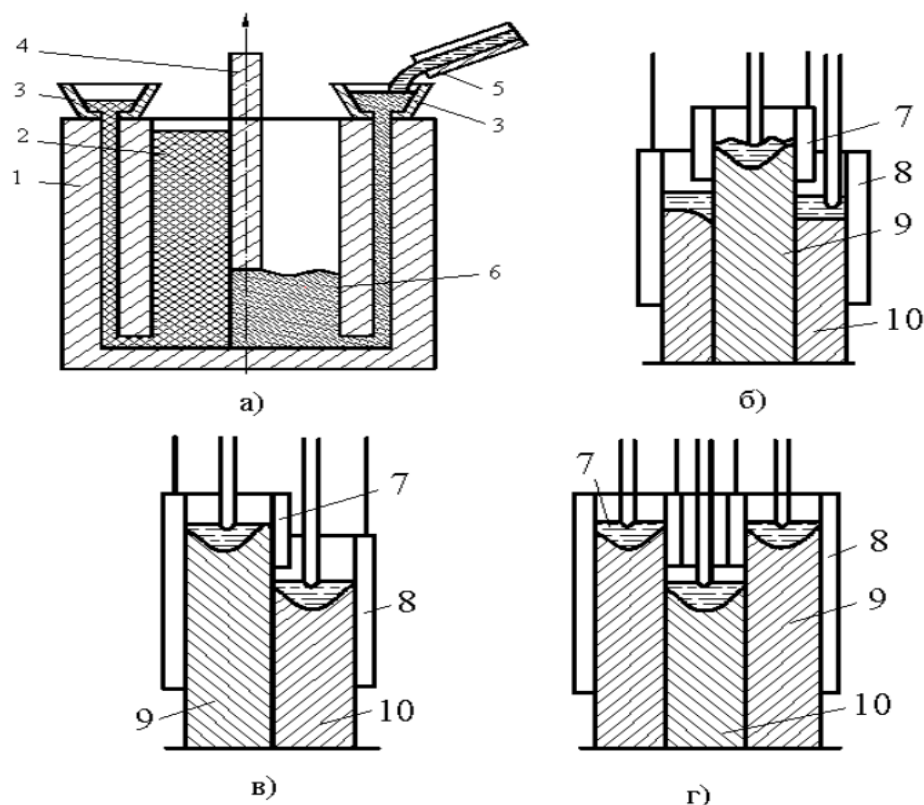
Способи послідовної відлитої металів: 1 - форма; 2 - залитий метал; 3 - розливна воронка; 4 - перегородка; 5 - жолоб; 6 - заливається метал; 7,8 - кристалізатор; 9,10 - метал (складові біметалу).
